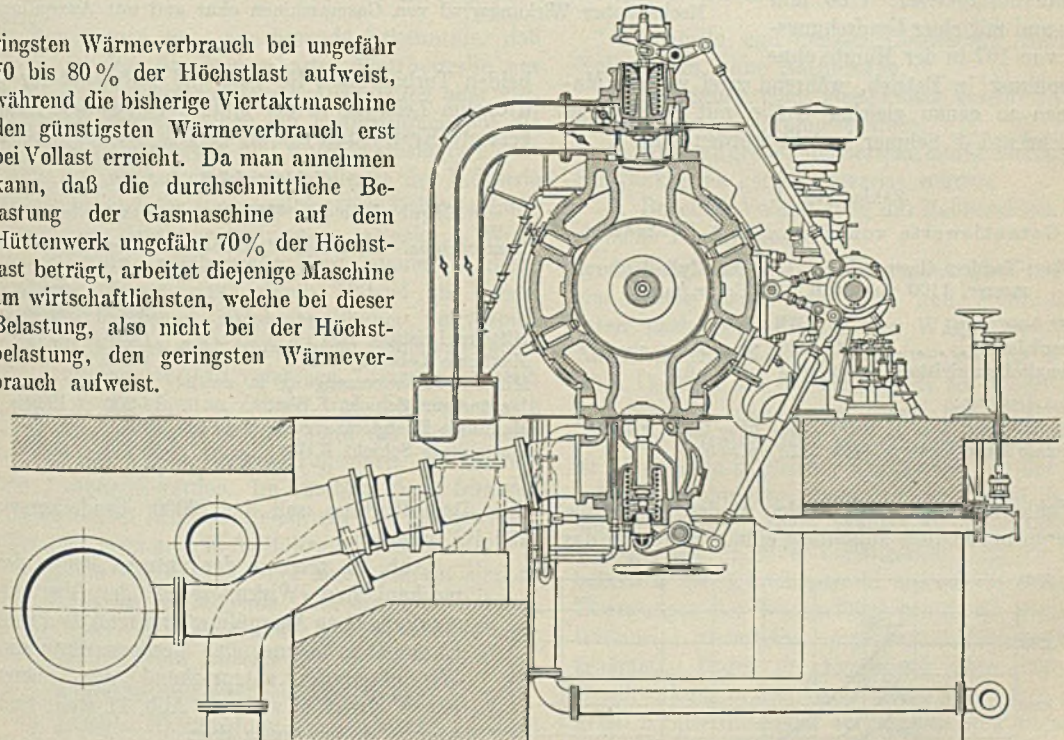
Querschnitt einer Gasmachine nach dem Ausspülverfahren, Bauart Ehrhardt & Sehmer.
